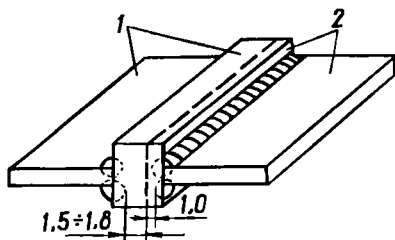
Сварное сталеалюминиевое соединение, полученное с помощью вставки из биметалла.
